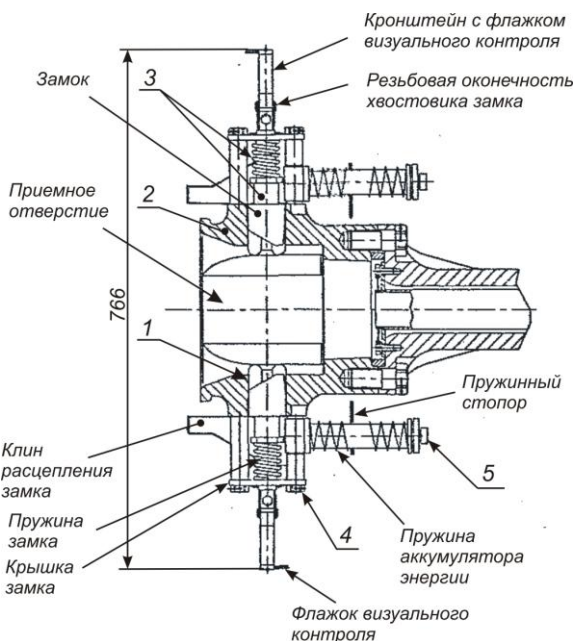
Сцепка с механизмами сцепления (вид в плане):
